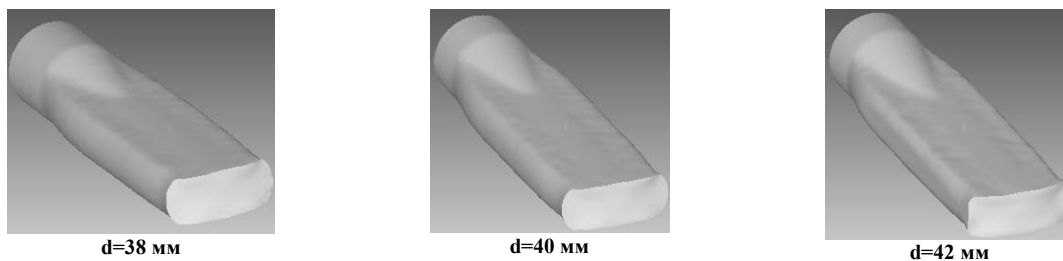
Здеформовані заготовки, які отримані з вихідних заготовок різного діаметра  $d$
